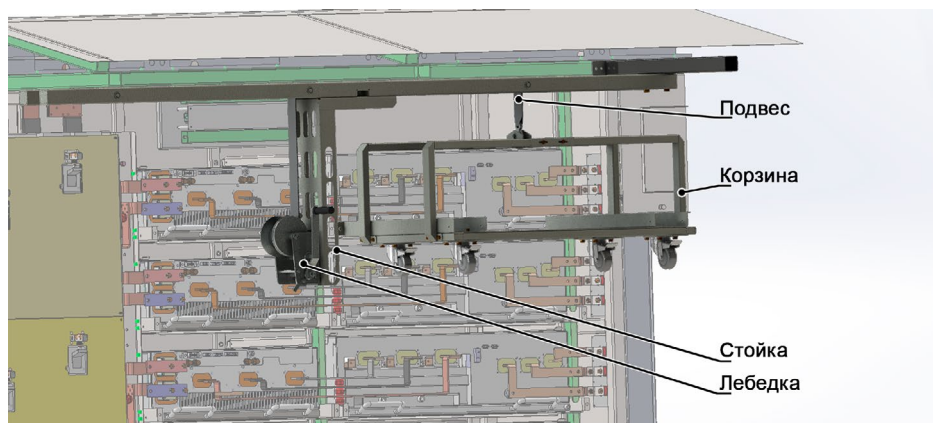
Грузоподъемное приспособление для транспортировки ячеек
